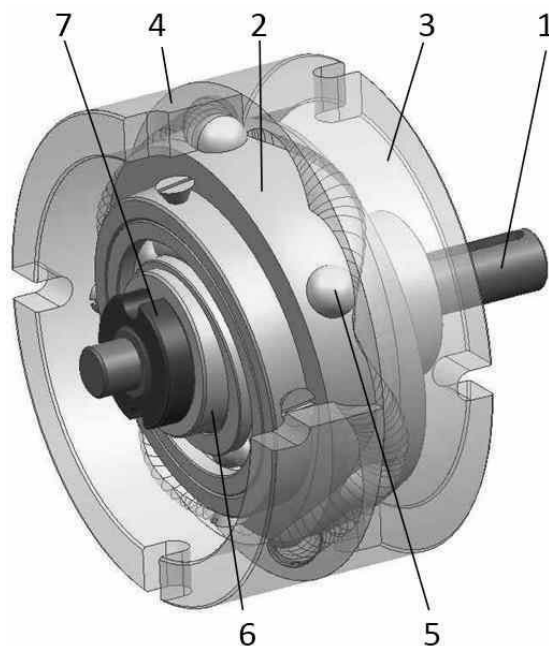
Конструктивная схема роликового зацепления: 1 – ведущий вал; 2 – генератор; 3 – левый наружный кулачок; 4 – правый наружный кулачок; 5 – ролик; 6 – косая шайба; 7 – гайка
